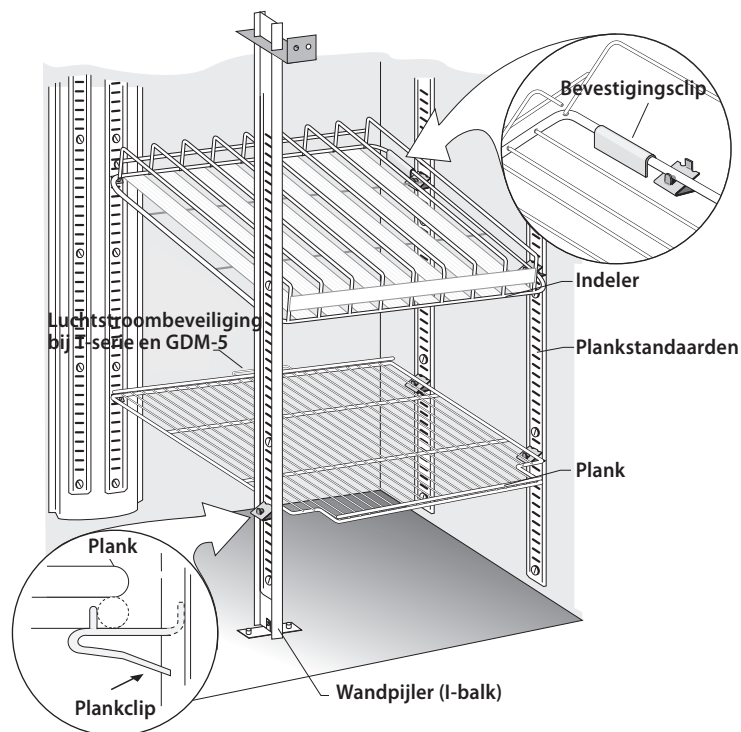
Het onderste lipje van de plankdrager zal strak aansluiten.
